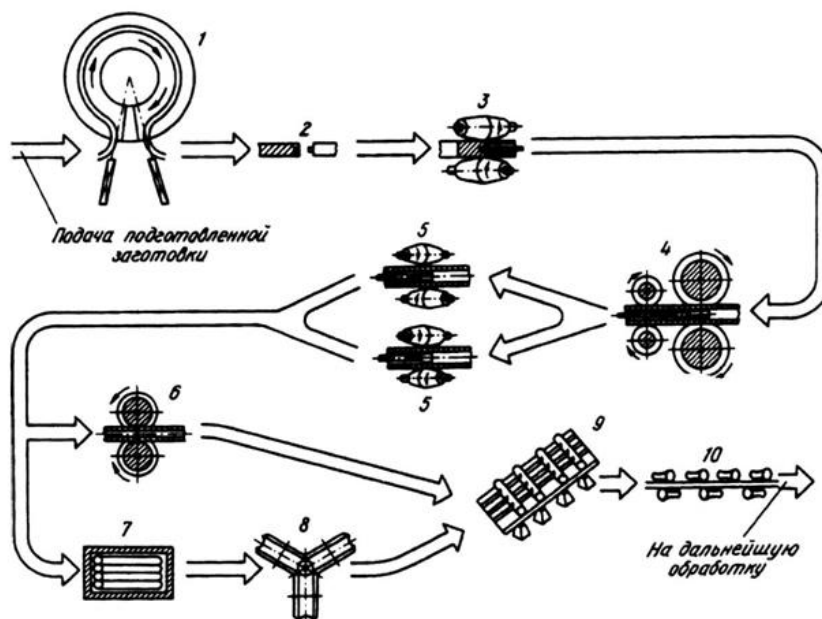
Схема технологічного процесу виробництва труб на ТПА з автоматичним станом: 1 - нагрів заготовок; 2 зацентровка заготовок; 3 - прошивка заготовок; 4 прокатка гільз в трубу; 5 - обкатка труб; 6 калібрування труб; 7 - проміжний підігрів труб; 8- редукування труб; 9-охолодження труб; 10 правка труб.
